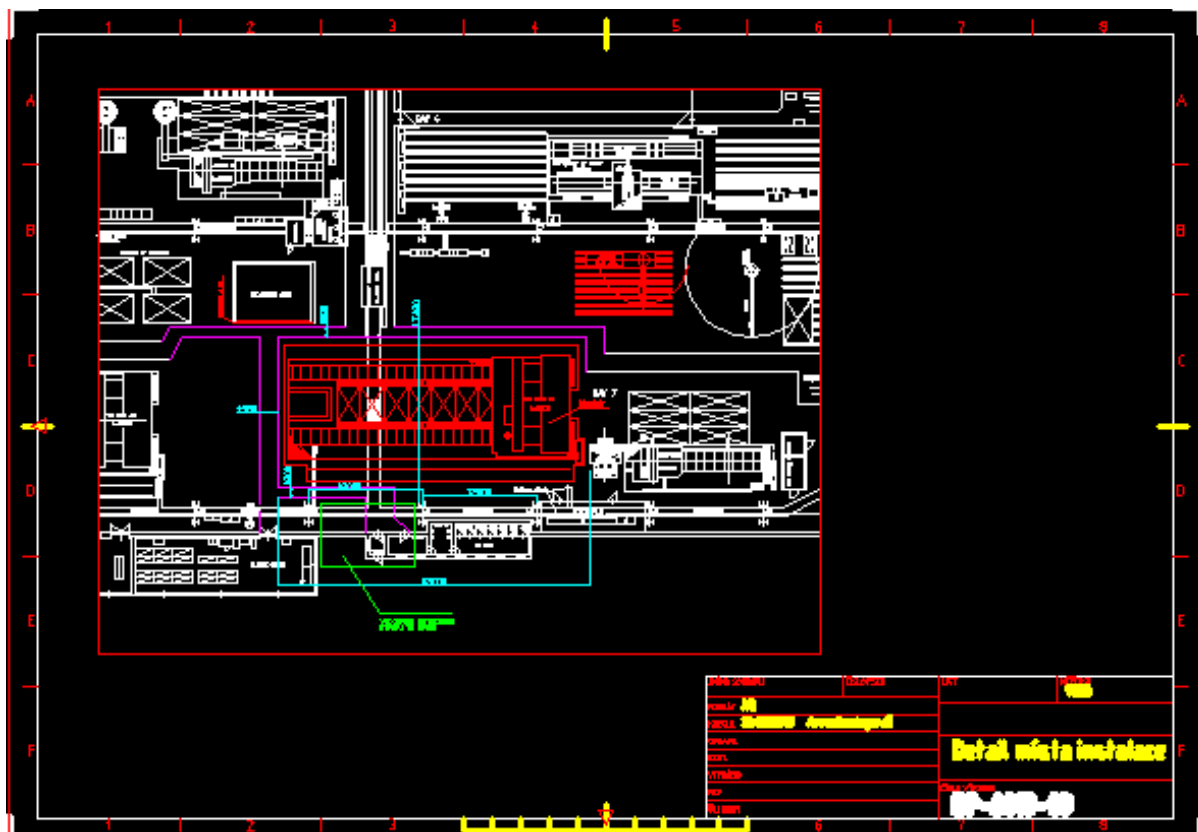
Náhled vypracovaného schematického layoutu stávajícího stavu
